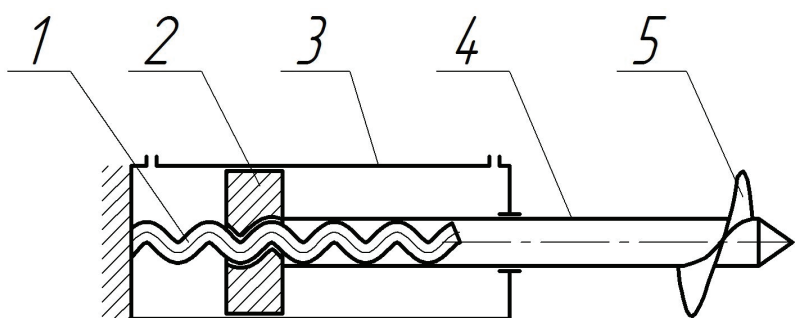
Схема гидроцилиндра с поступательно-вращательным движением штока: 1 – винт; 2 – гайка-поршень; 3 – гидроцилиндр; 4 – шток; 5 – винтовой наконечник.
